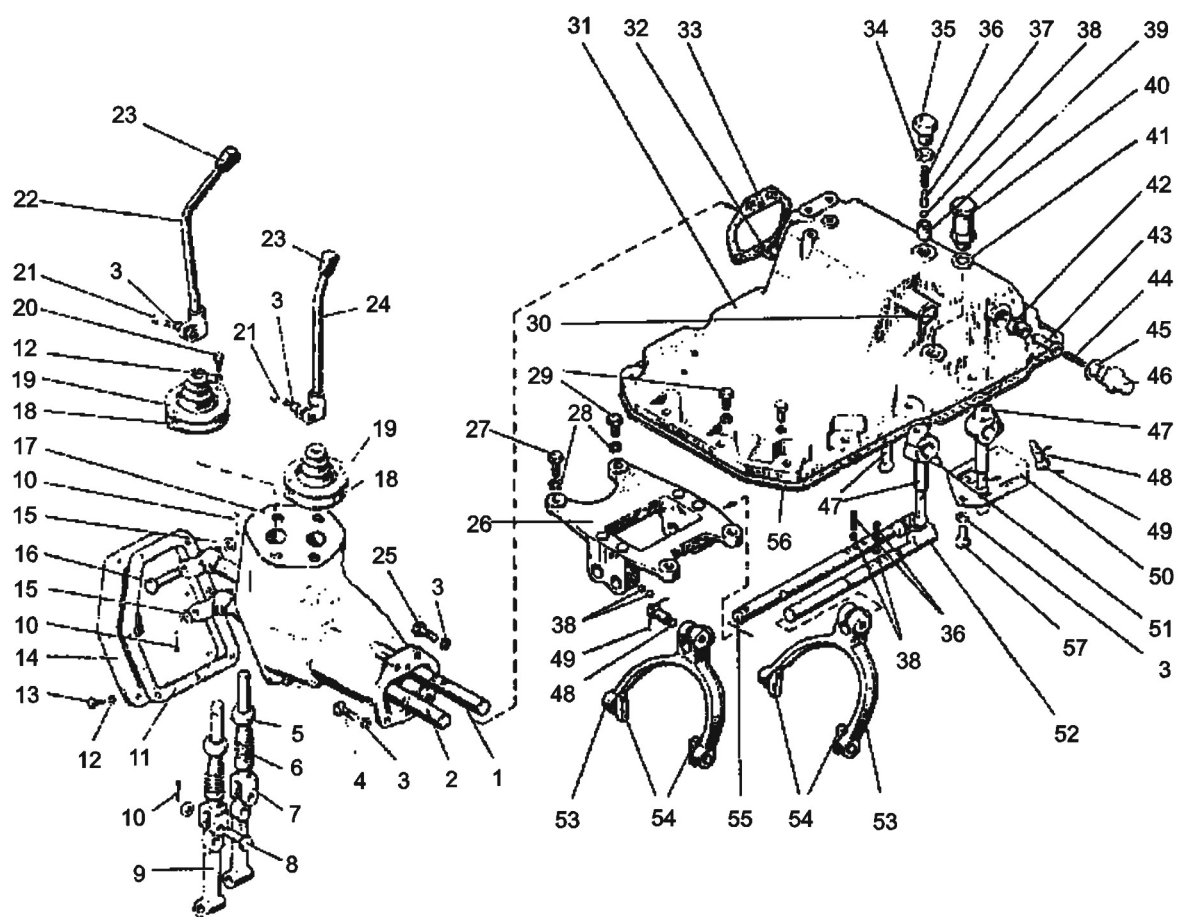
Коробка передач – Механизм управления. Корпус. Вилка. Ограничитель
